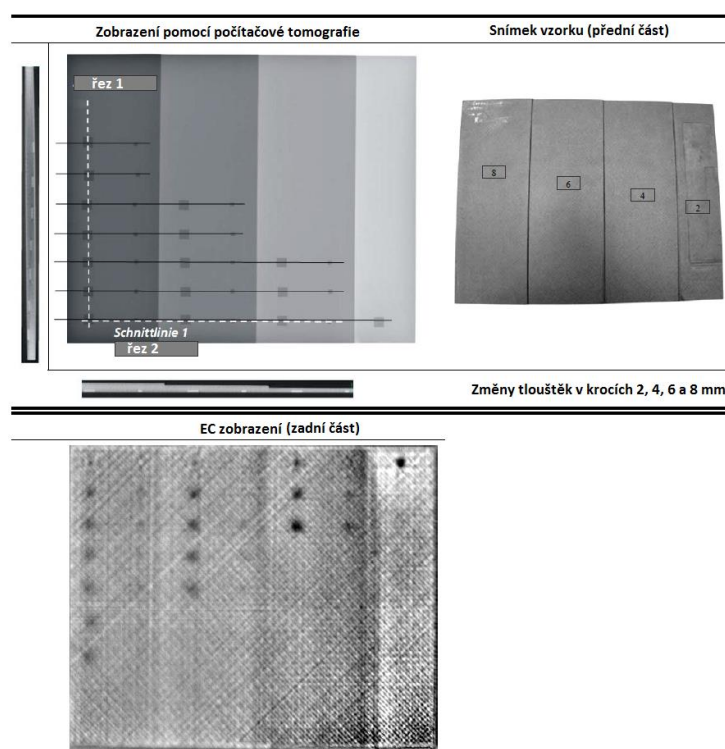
Ukázka zobrazení jednotlivých poškození pomocí zobrazení C-sken [12]
